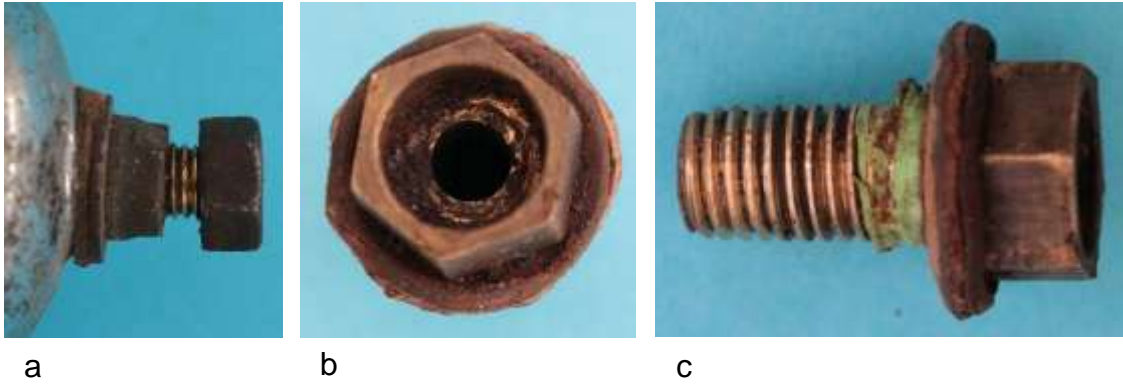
Spurlager: a) Kabelanschlussbolzen, b) Bohrung für die Welle, c) Kombination des Spurlagers und des Kabelanschlussbolzens
